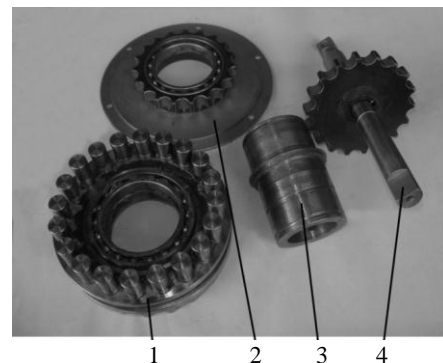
Вид основных деталей прецессионного редуцирующего механизма лебедки после проведения эксплуатационных испытаний: 1 – сепаратор с роликами; 2 – звездочка подвижная; 3 – кривошип; 4 – звездочка неподвижная с основным валом
